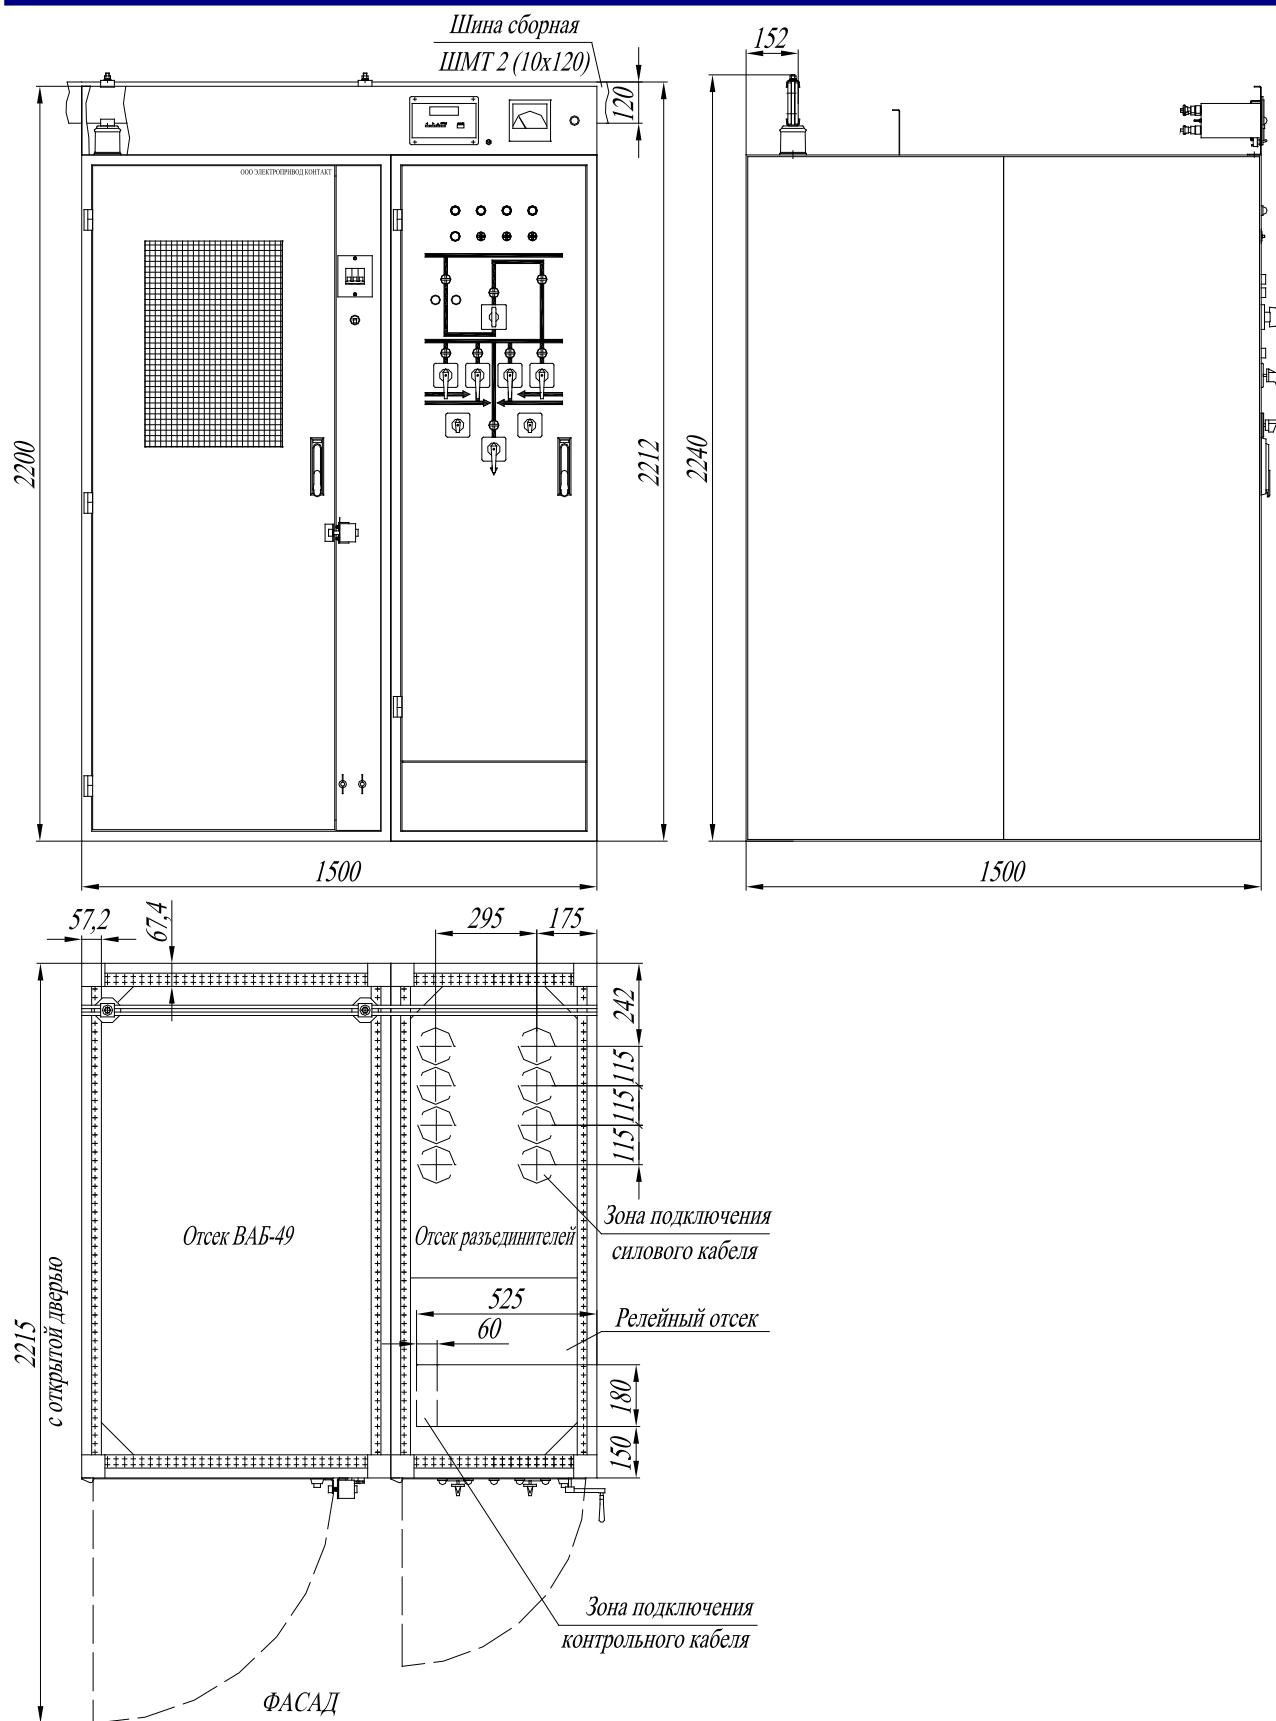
Шкаф резервной питающей линии на 5 разъединителей.
